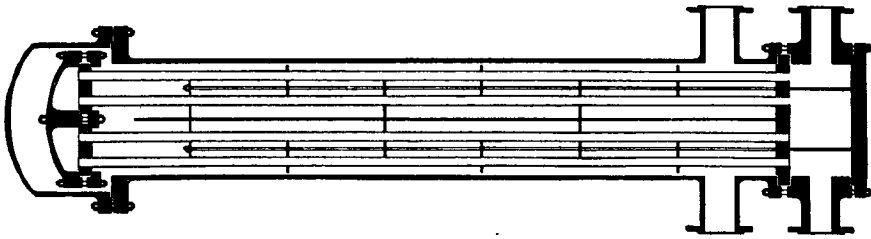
Intercambiador 2-4 de cabezal flotante con deflector fijo. (*Patterson Foundry & Machine Co.*)
